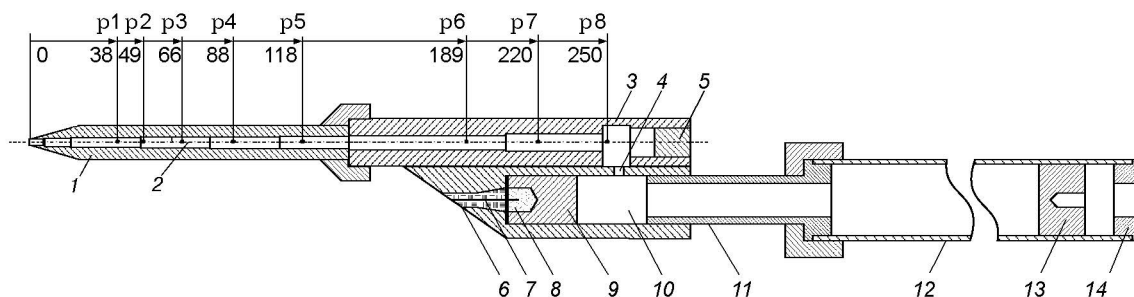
Схема модели для отбора пробы газа из рабочей части:
